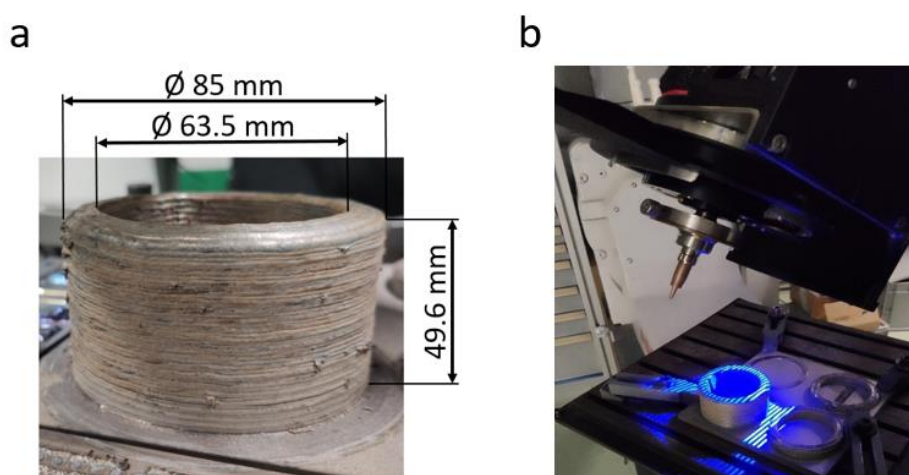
Digitalización de geometría mediante escáner basado en luz estructurada. a) Pieza cilíndrica fabricada mediante LMD con aporte de hilo de titanio Ti6Al4V; b) escaneo de pieza cilíndrica desde una de las posiciones del robot.
